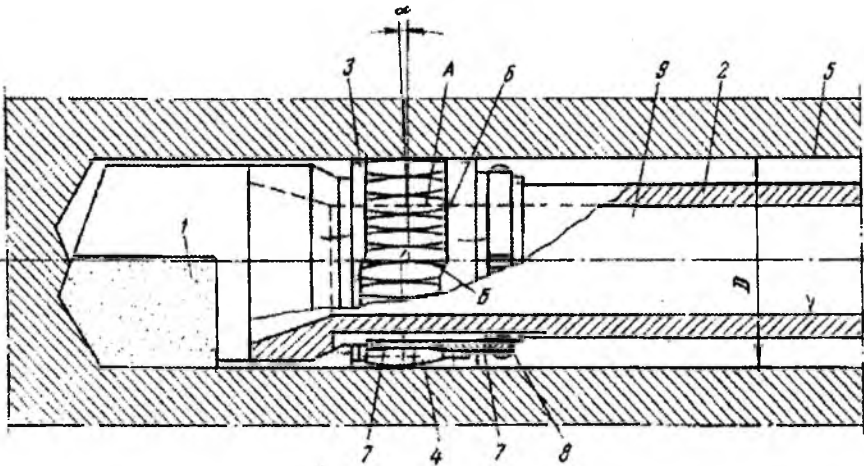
Свердло для глибокого свердління із самоподачею
